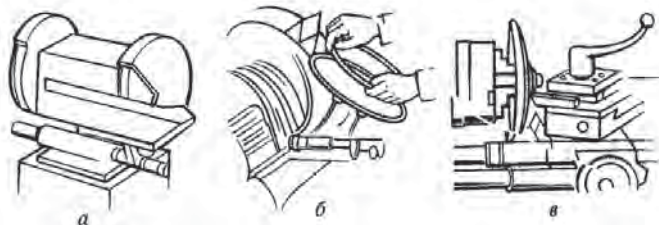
Приспособления для заточки почворезущих рабочих органов: а — лемехов; б, в — дисковых ножей плугов
